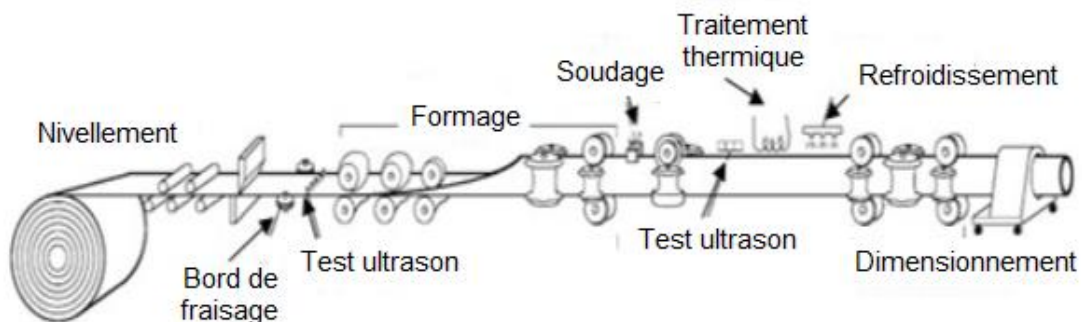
Technique de fabrication des tubes soudés en spirale [9]
